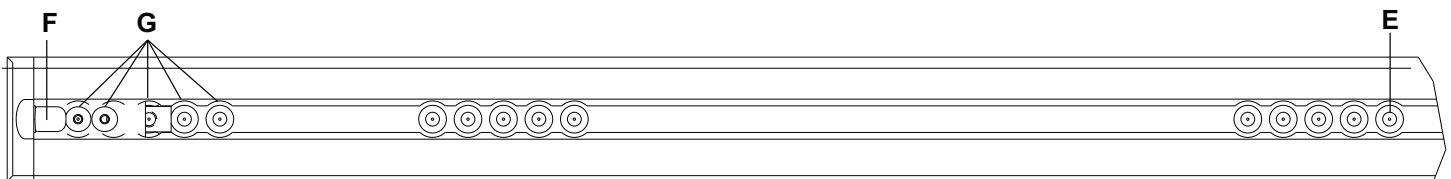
Posición del posicionador de la placa de suelo - extremo de los pies
